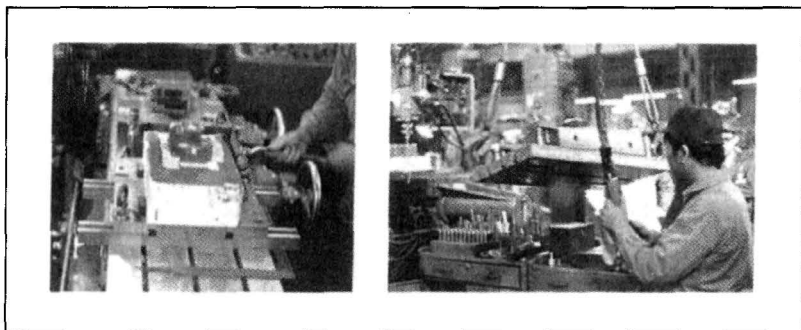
Трафарет изделия центруется на вспомогательной оснастке, и готовая сборка устанавливается на станок
